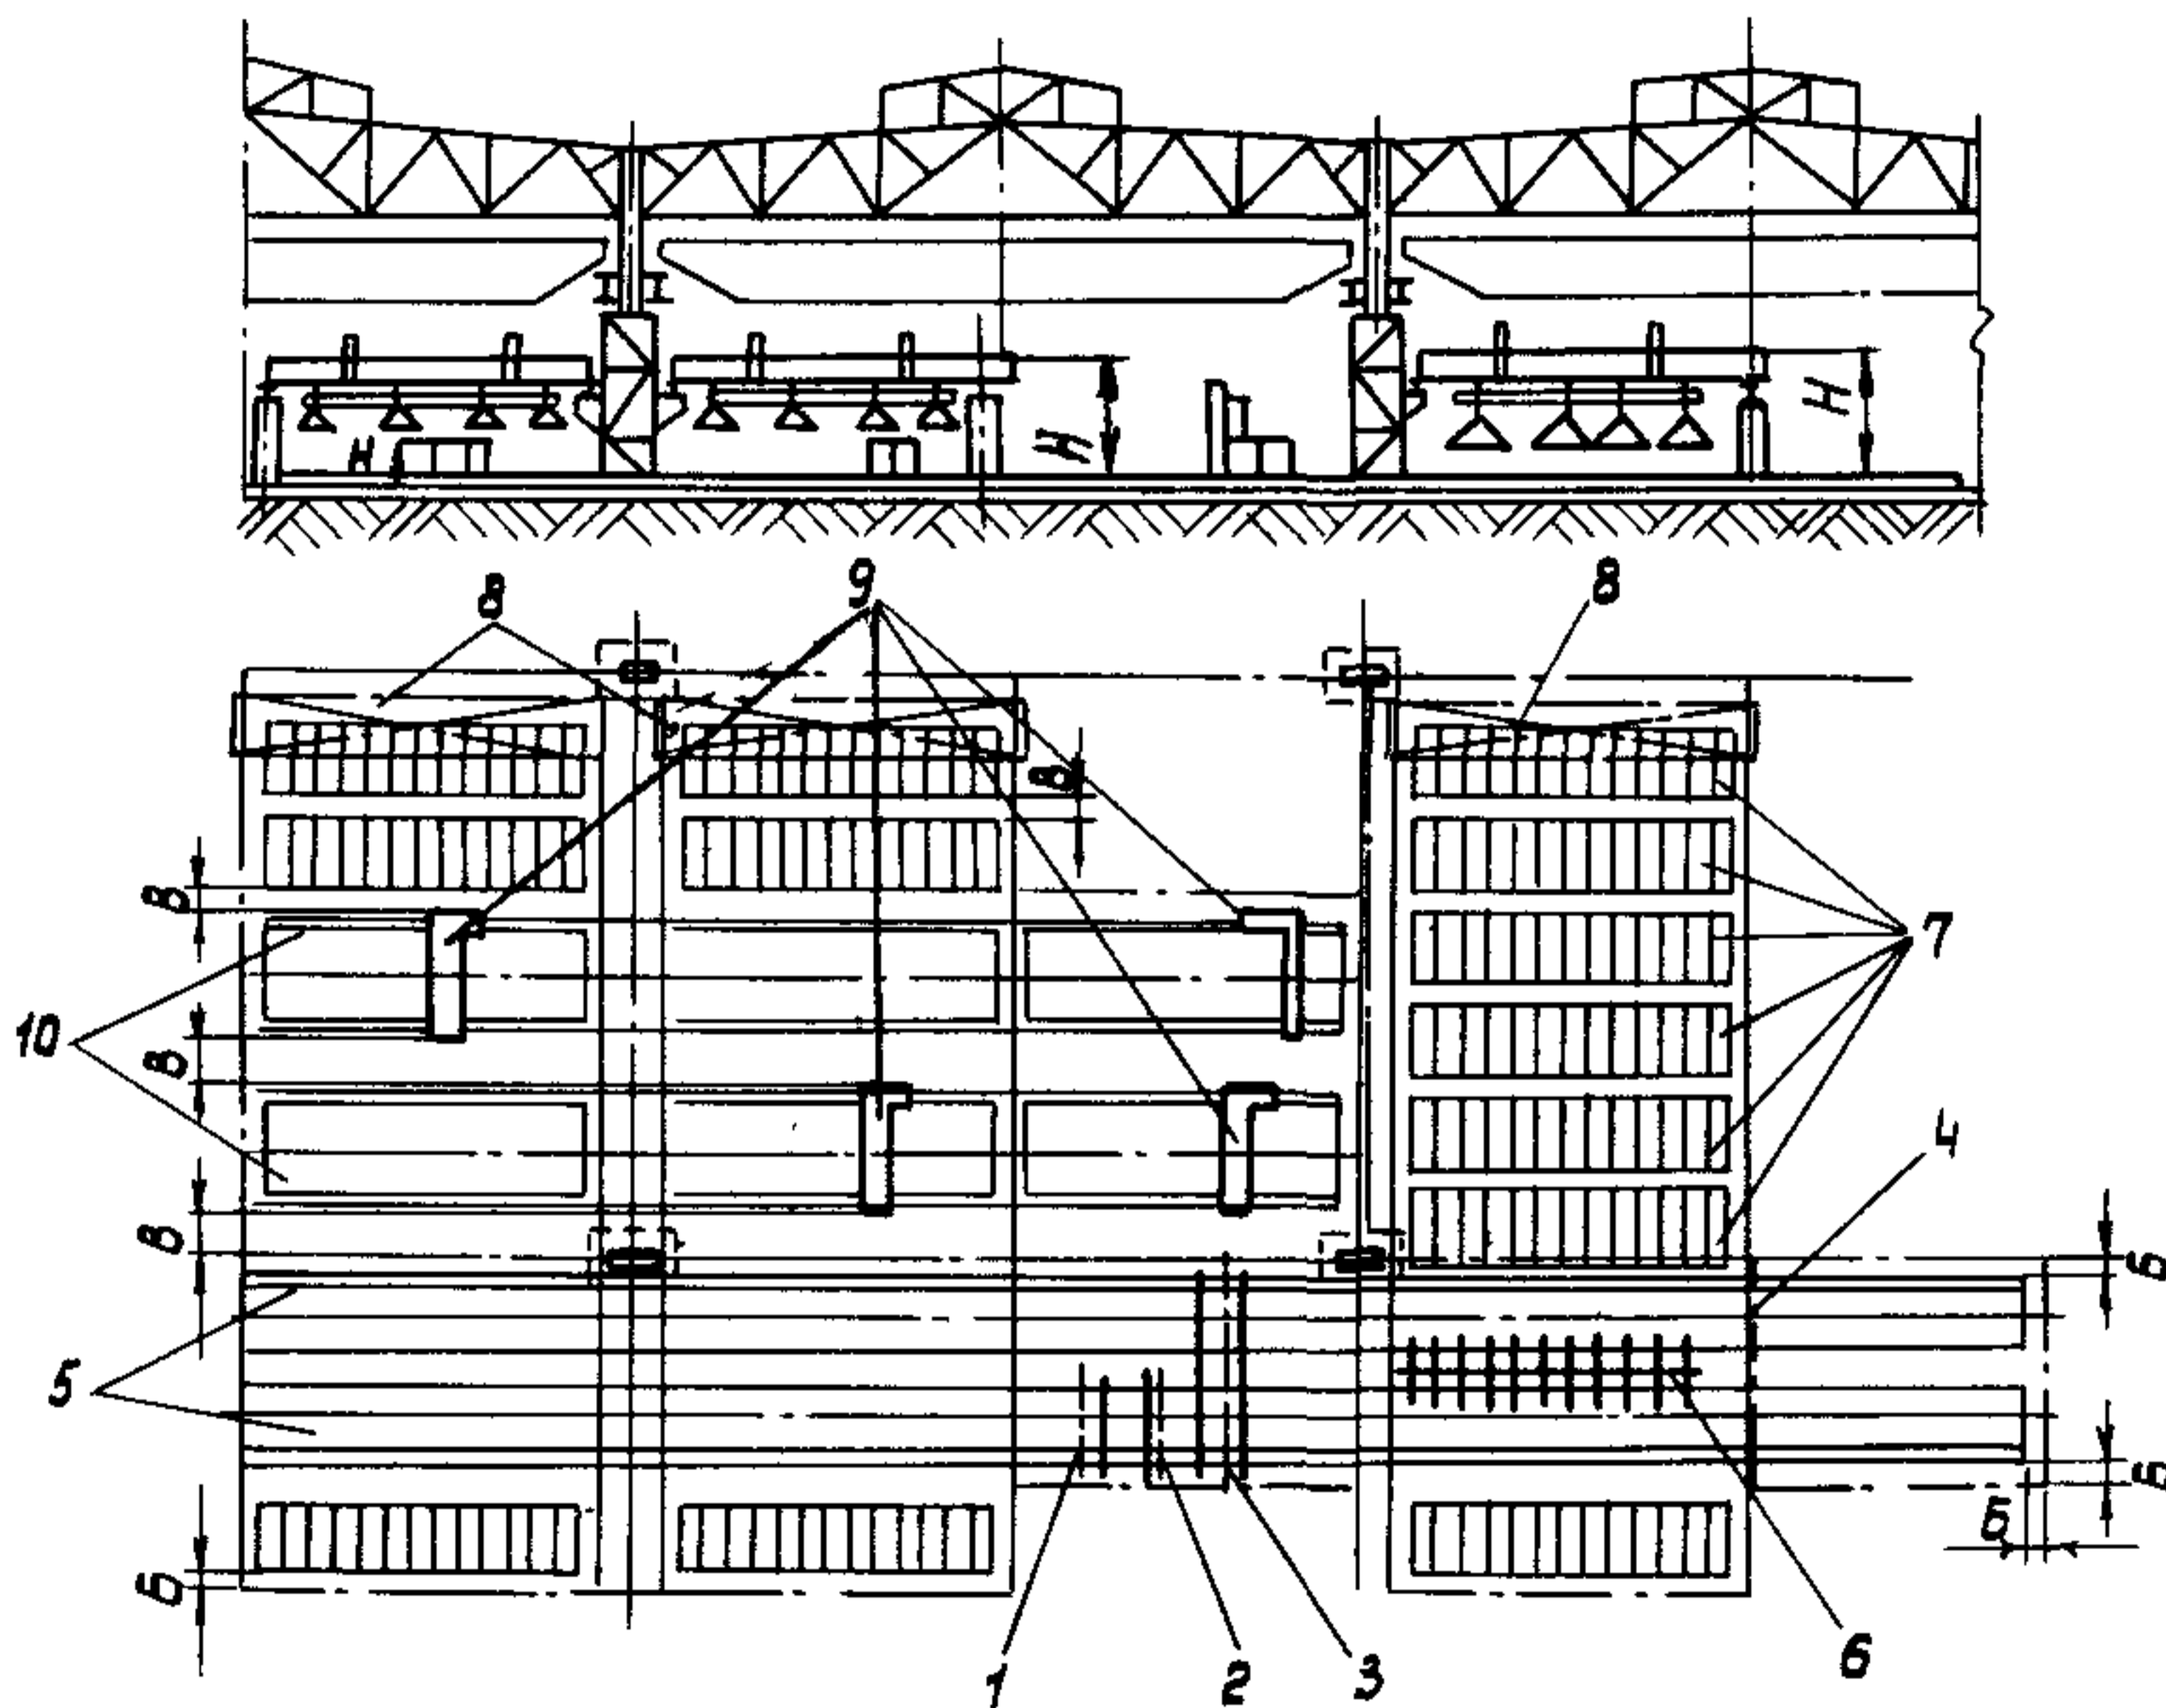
Размещение поточной линии стыковки и резки стального листа:
